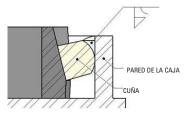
Procedimiento de Soldadura - Corte Transversal
